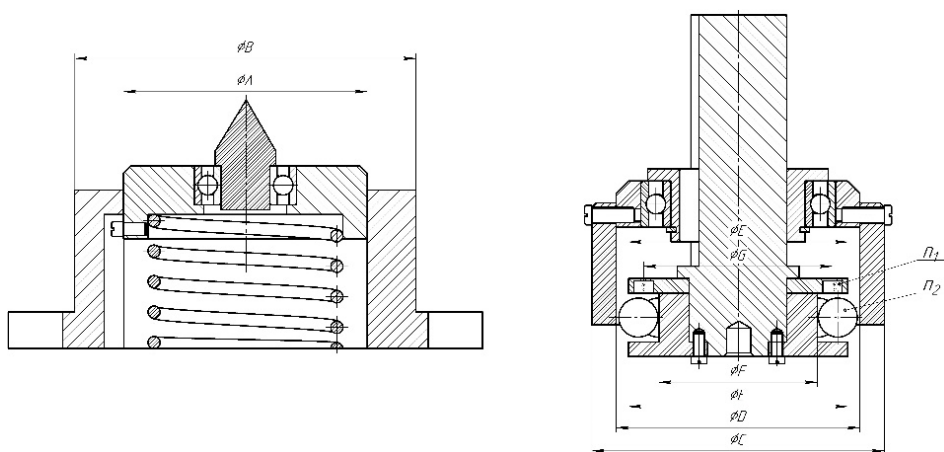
Модульная конструкция устройства для отделочно-упрочняющей обработки
